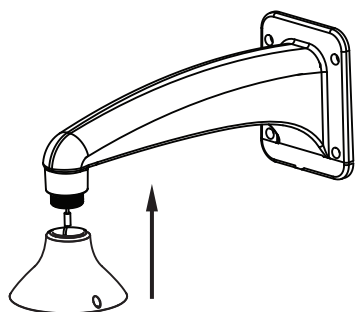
Cappuccio di montaggio fissato alla staffa a parete
